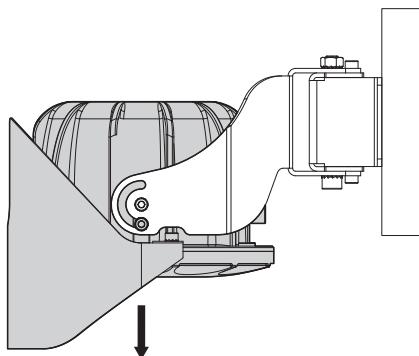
Installazione a parete (rotazione verticale, -90°).
